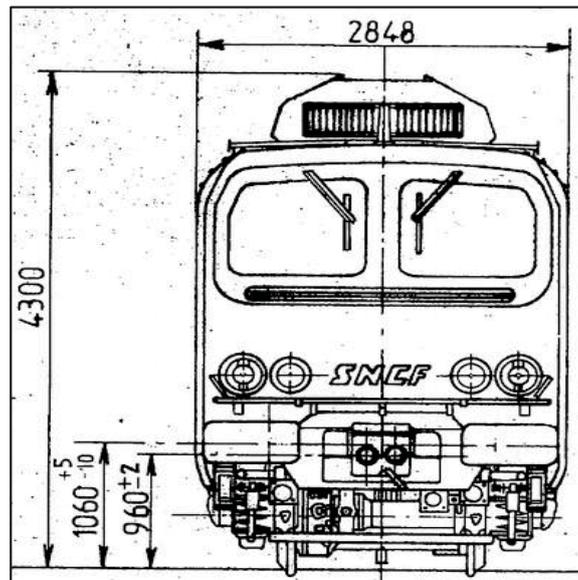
Dimensions de la face avant de la motrice (en mm)
